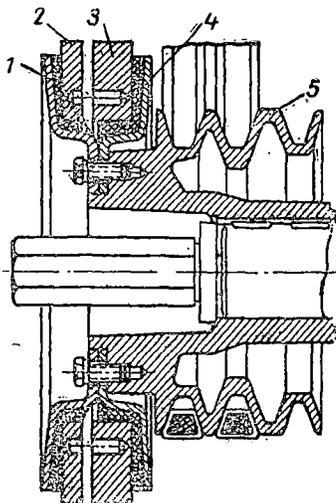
Гаситель крутильных колебаний коленчатого вала двигателя:
